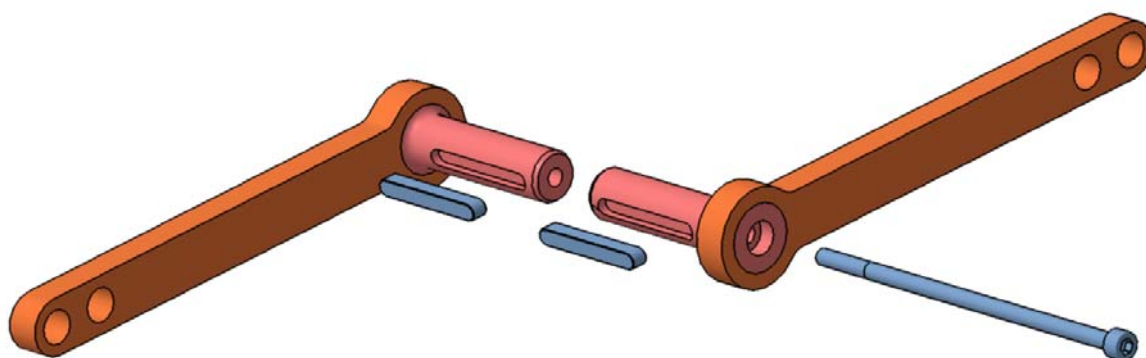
CAD Zeichnung der starren Kurbeln.
